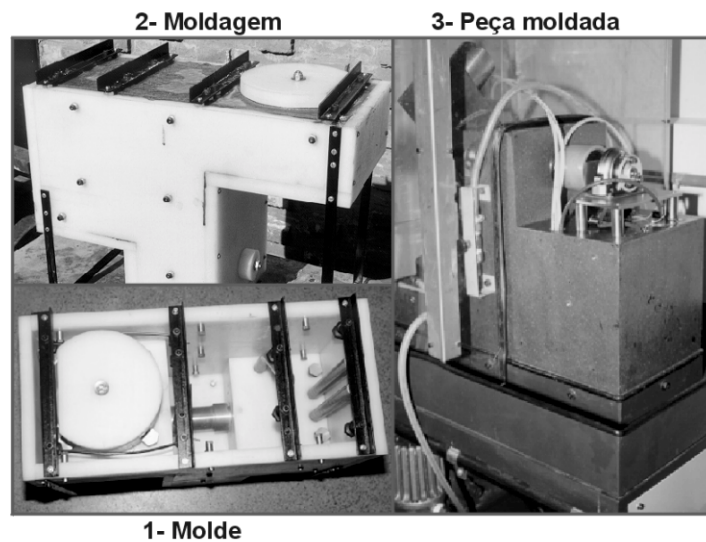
Molde e moldagem da estrutura da máquina geradora de esferas em granito sintético.
